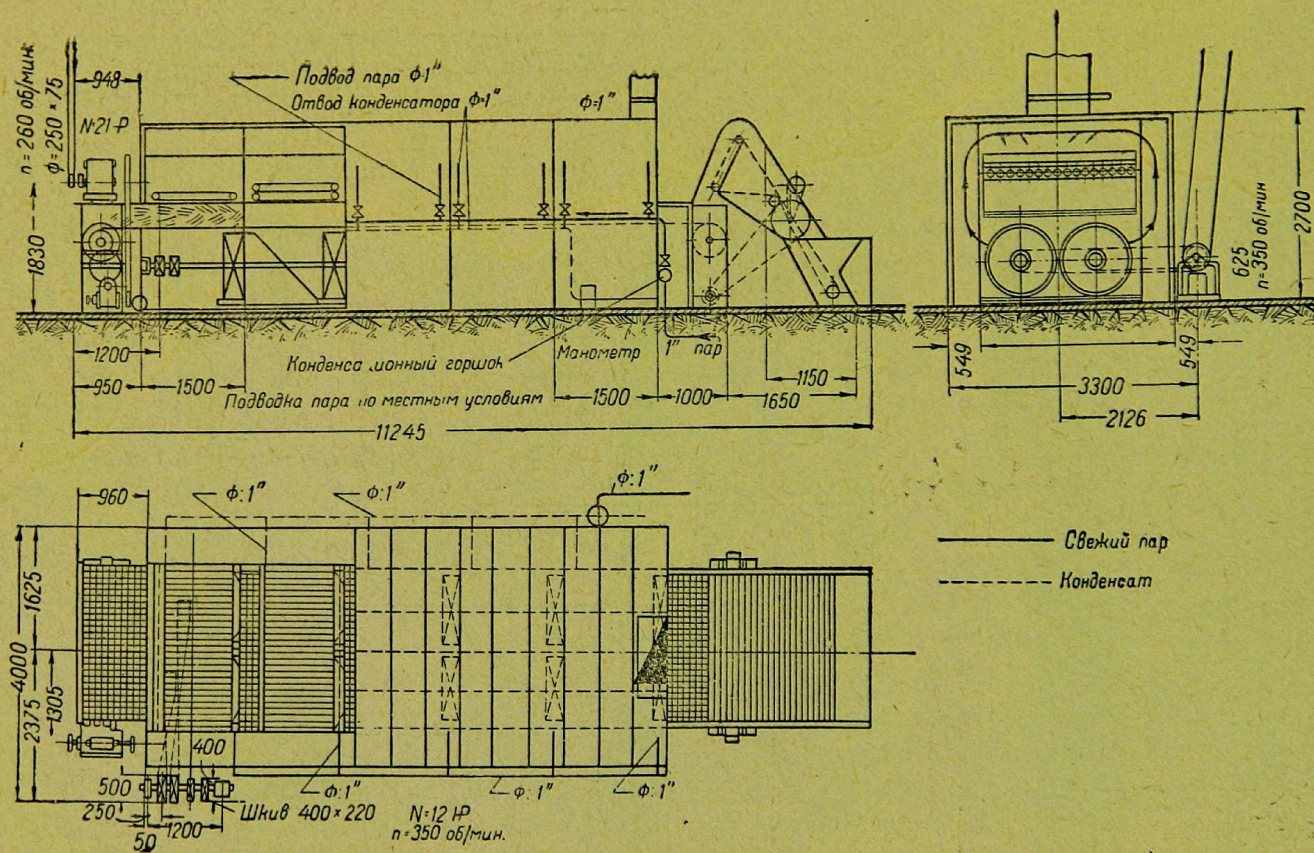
Сушилка Вено-Шильде (продольный разрез, поперечный разрез и план)
